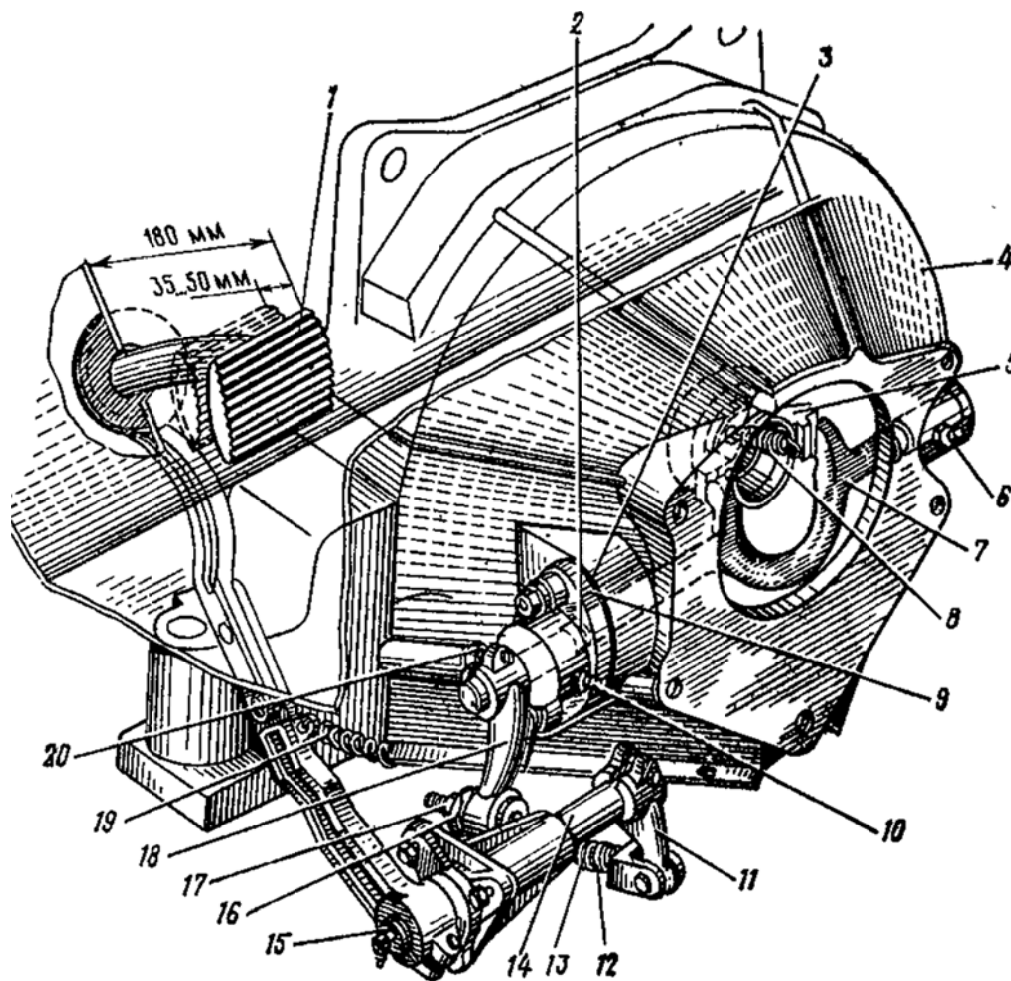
Привод выключения сцепления автомобиля ЗИЛ-131:
